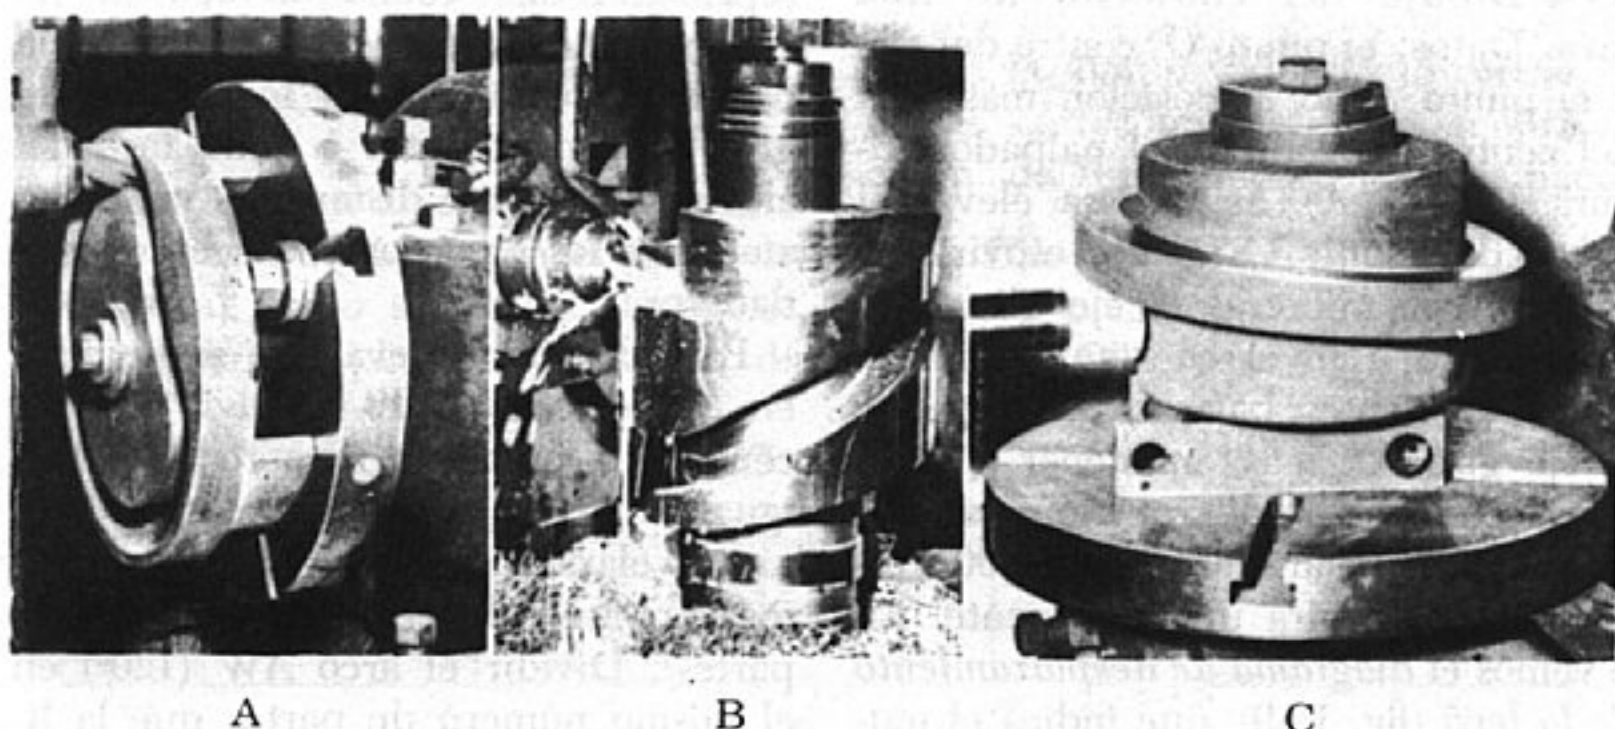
Mecanización de levas. (The Rowbottom Machine Company.)
